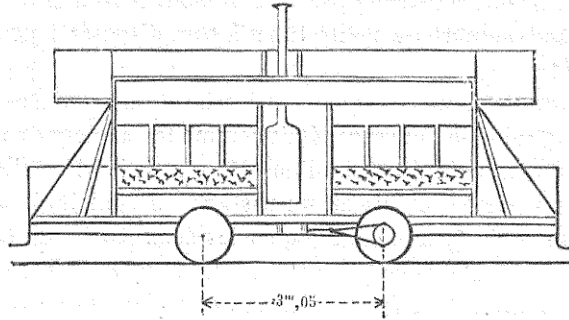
Car à vapeur de M. John Grantham, 1872.
